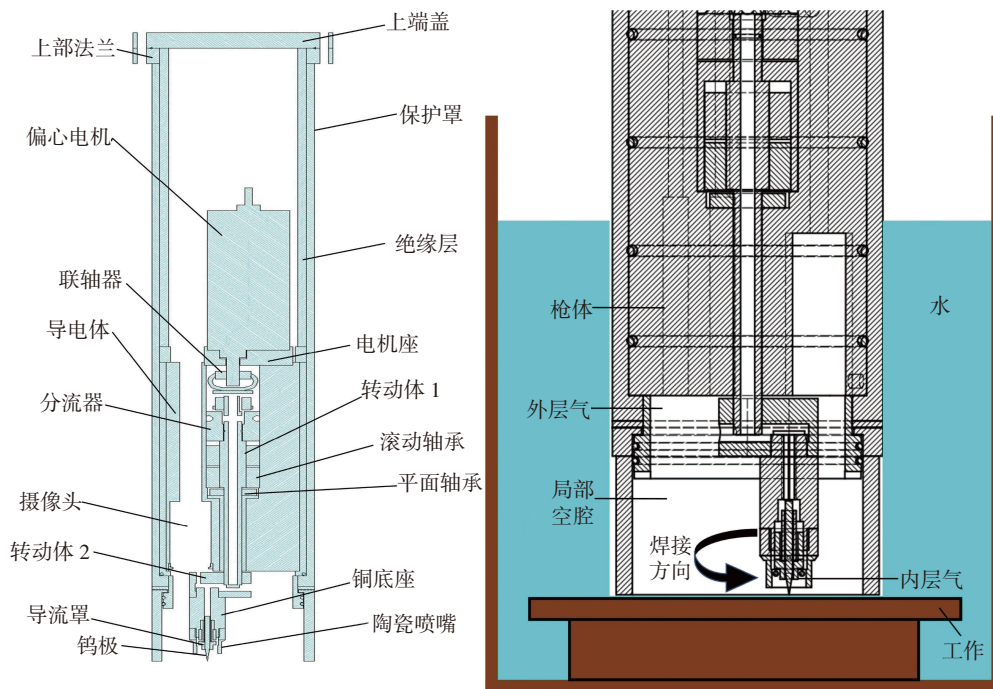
水下 TIG 焊系统结构及焊接过程示意图
